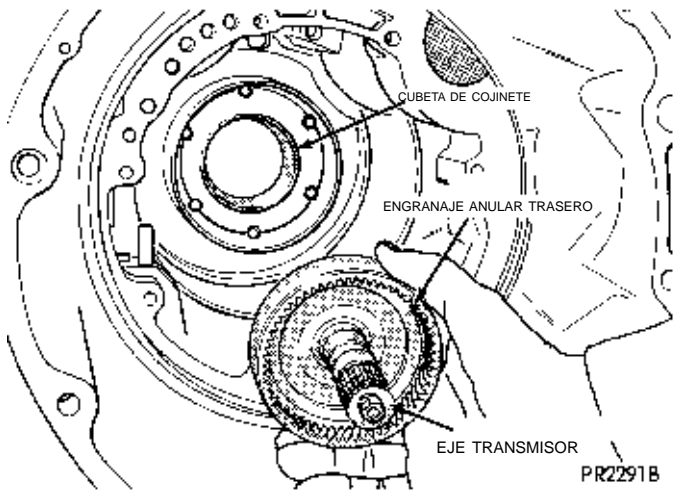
Desmontaje del conjunto del eje transmisor y el engranaje anular trasero
